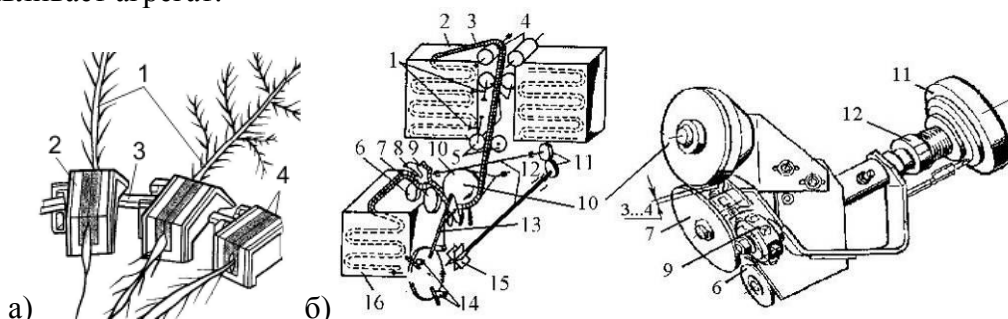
Схема лесопосадочного автомата: а): 1 – сеянцы; 2 – звено кассеты; 3 – соединительный элемент; 4 – резиновый зажим; б): 1 – пружины; 2 – контейнер; 3 – кассетный сеянцедержатель; 4 – направляющий валик; 5 – ролик; 6, 7 – прижимные ролики; 8 – отсекатель; 9 – ведущая звездочка; 10 – ролик профильный; 11 – зубчатые колеса; 12 – вал привода; 13 – посадочный аппарат; 14 – упор; 15 – крыльчатка привода протяжки; 16 – контейнер с отработанной кассетой
